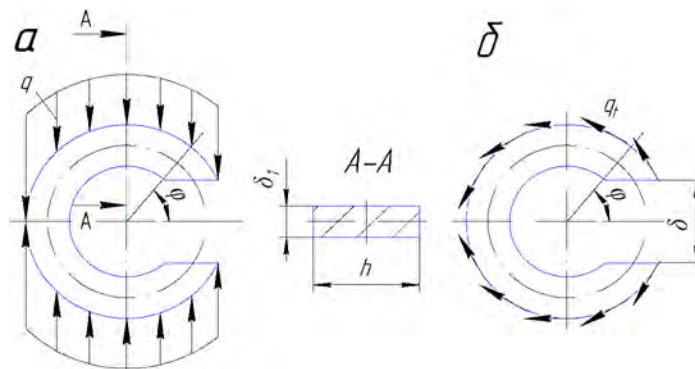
Розрахункова схема циліндричної розрізаної пружини
